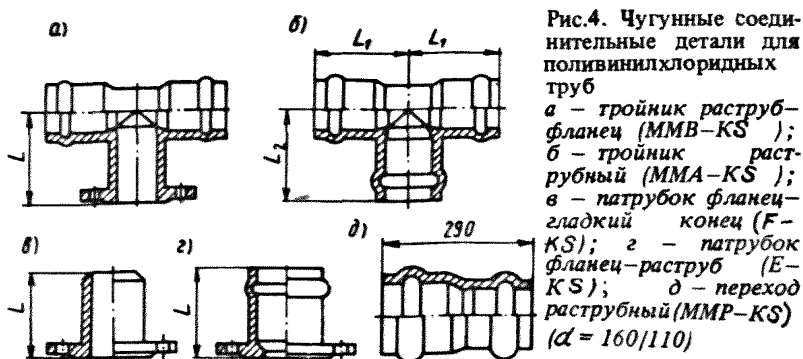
Чугунные соединительные детали для поливинилхлоридных труб
